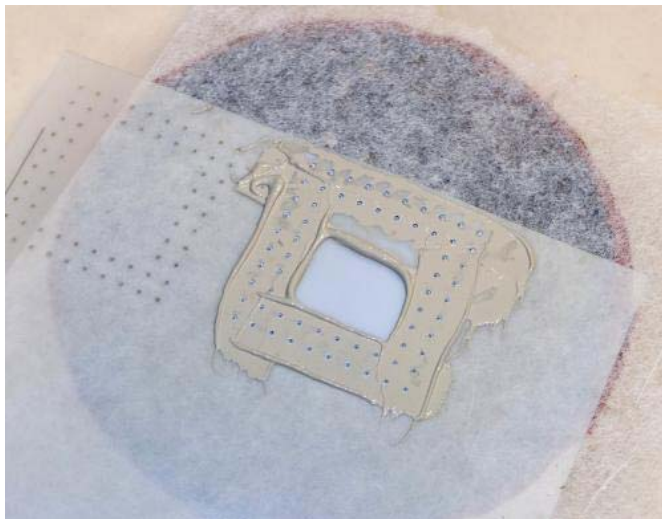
Příprava otvorů v laserem předřezaném LTCC substrátu
